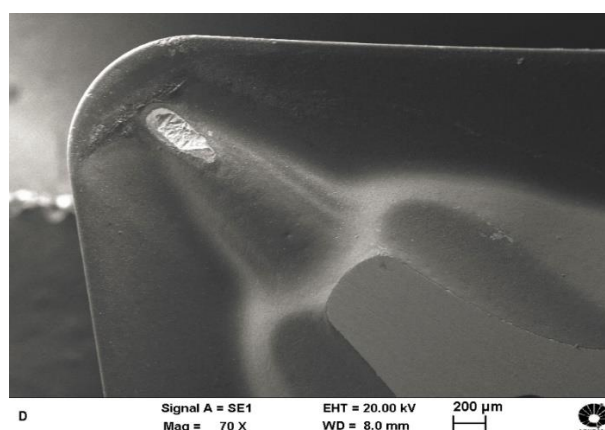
Superfície de saída da ferramenta de corte, emulsão, superfície de saída, velocidade de corte de 288 m/min.
